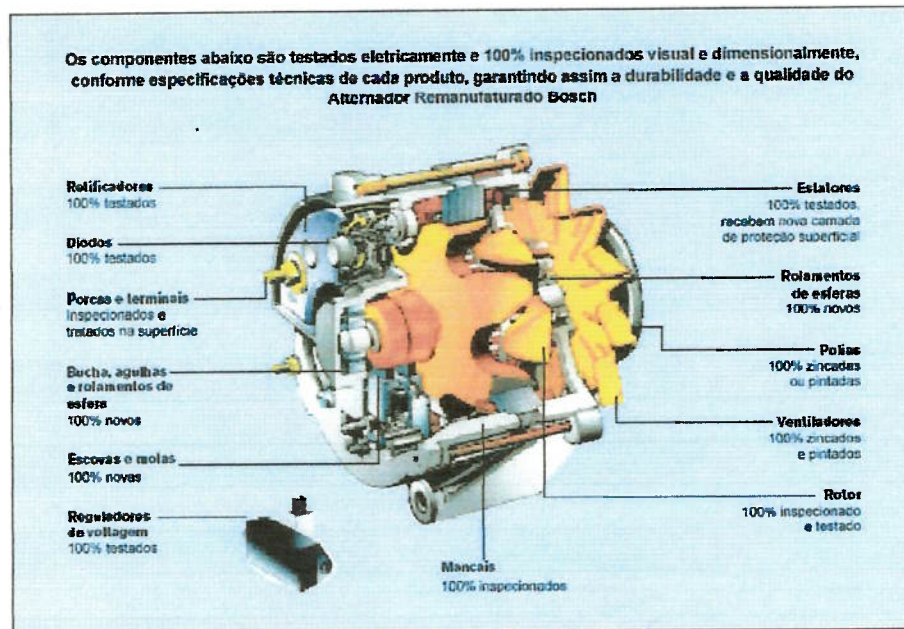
Alternador remanufaturado BOSCH, [60].
